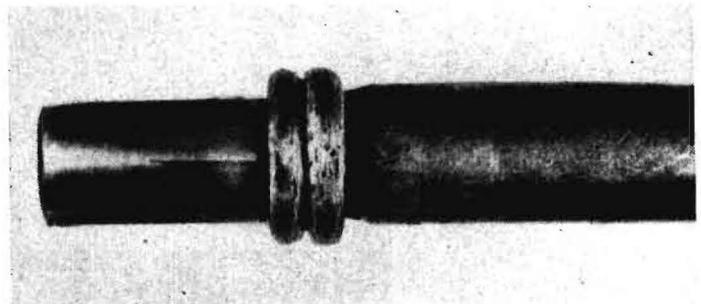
Instandsetzungsschweißung durch Reibschweißen
